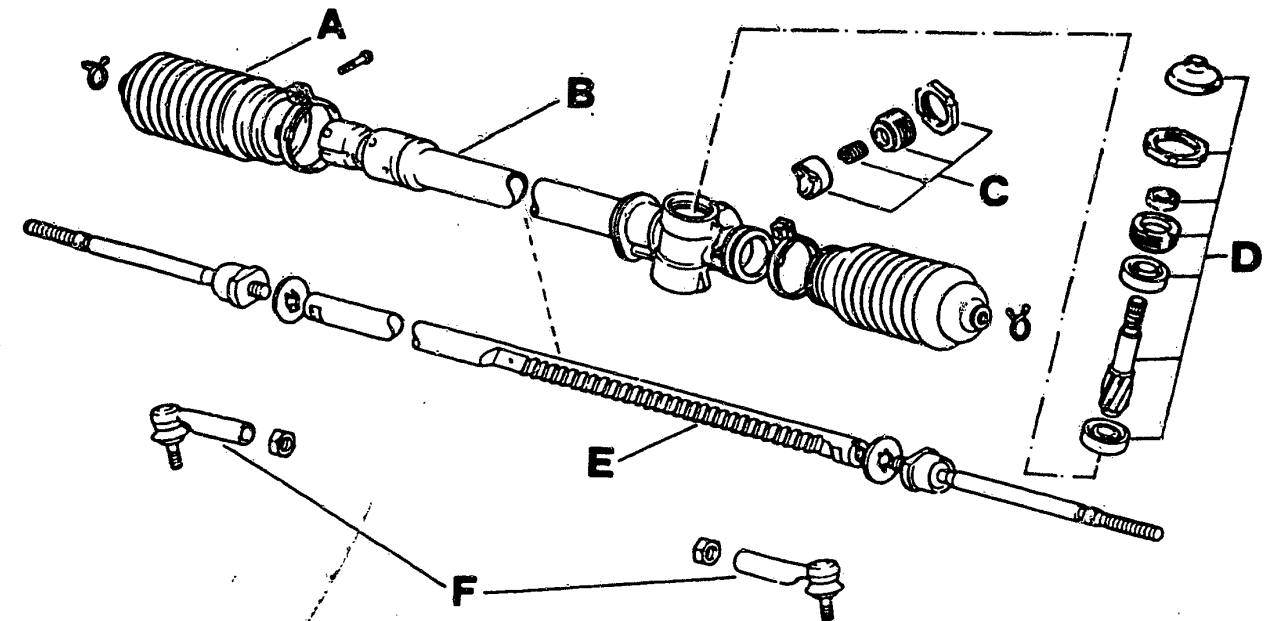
Einzelteile der Zahnstangenlenkung: A Schutzgummi – B Gehäuse – C Druckstück – D Ritzel mit Lagerung – E Zahnstange – F Spurstangengelenke.
